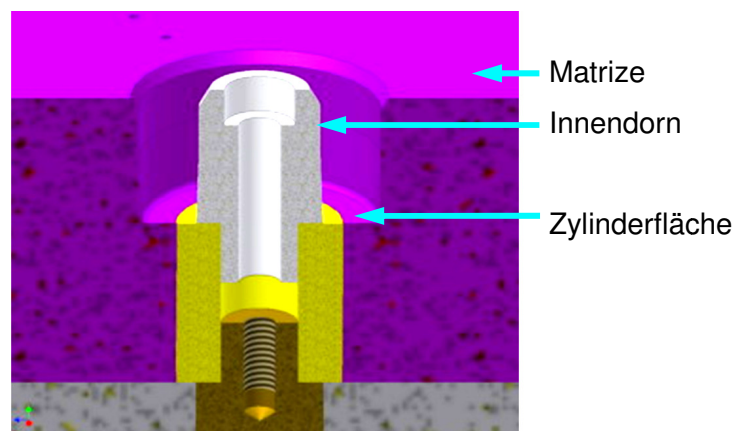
Detail der Matrize für Zylinder-Proben mit Dorn.
